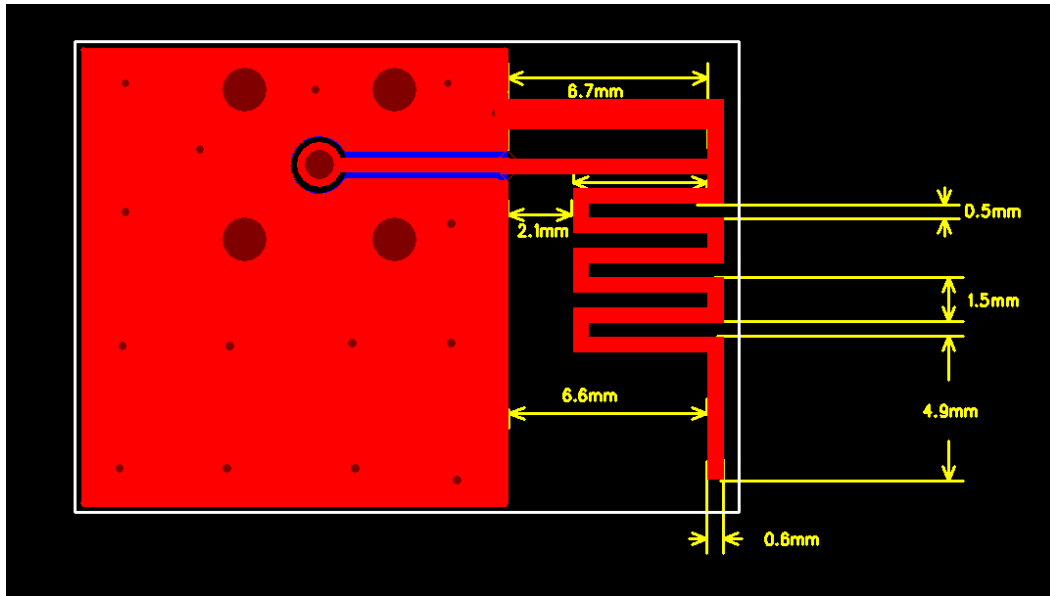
Normal_PIFA 天线的 PCB 尺寸
